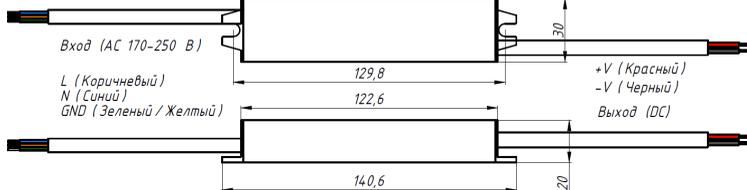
Габаритные размеры блока питания Geniled GL-12V40WM67.
